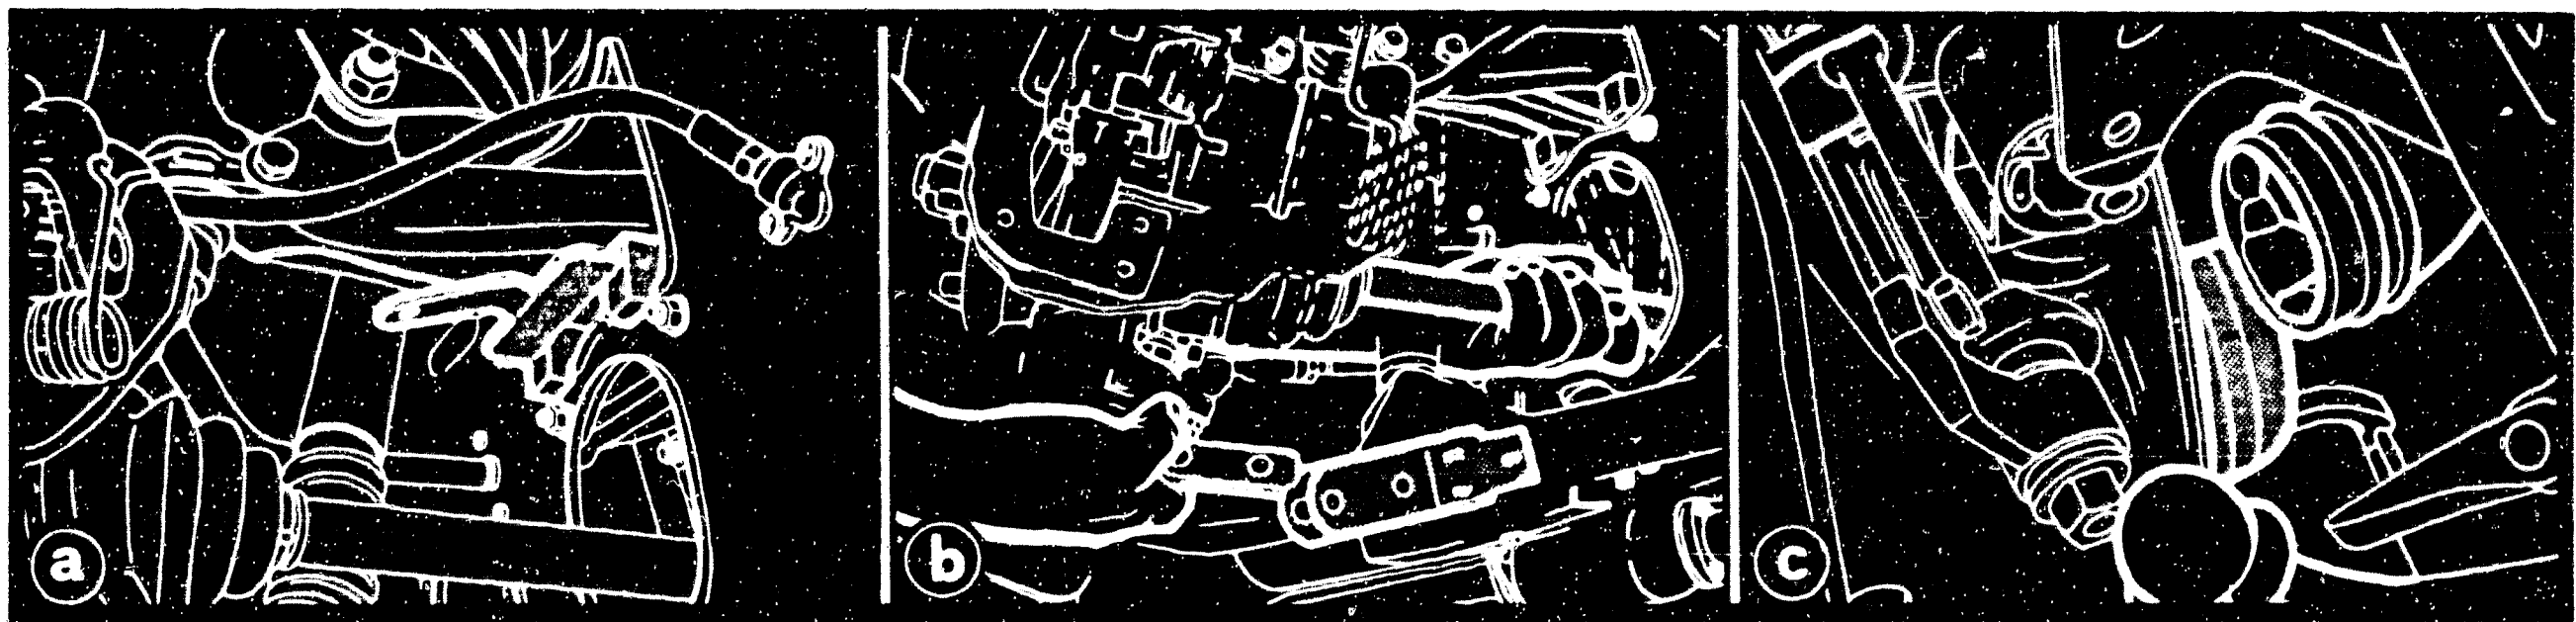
Motorausbau: a) Der Federentlastungsbugel (Spezialwerkzeug 8393209) wird vom Radkasten aus unter den rechten oberen Querlenker gelegt, um die Feder beim Anheben des Fahrzeugs zu entlasten. – b) Die rechte
